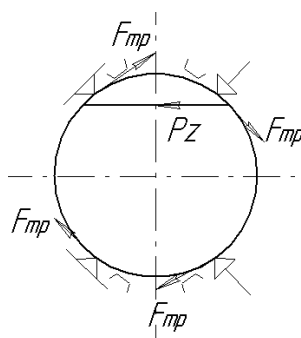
Схема для розрахунку сили закріплення  $W$  при фрезеруванні
